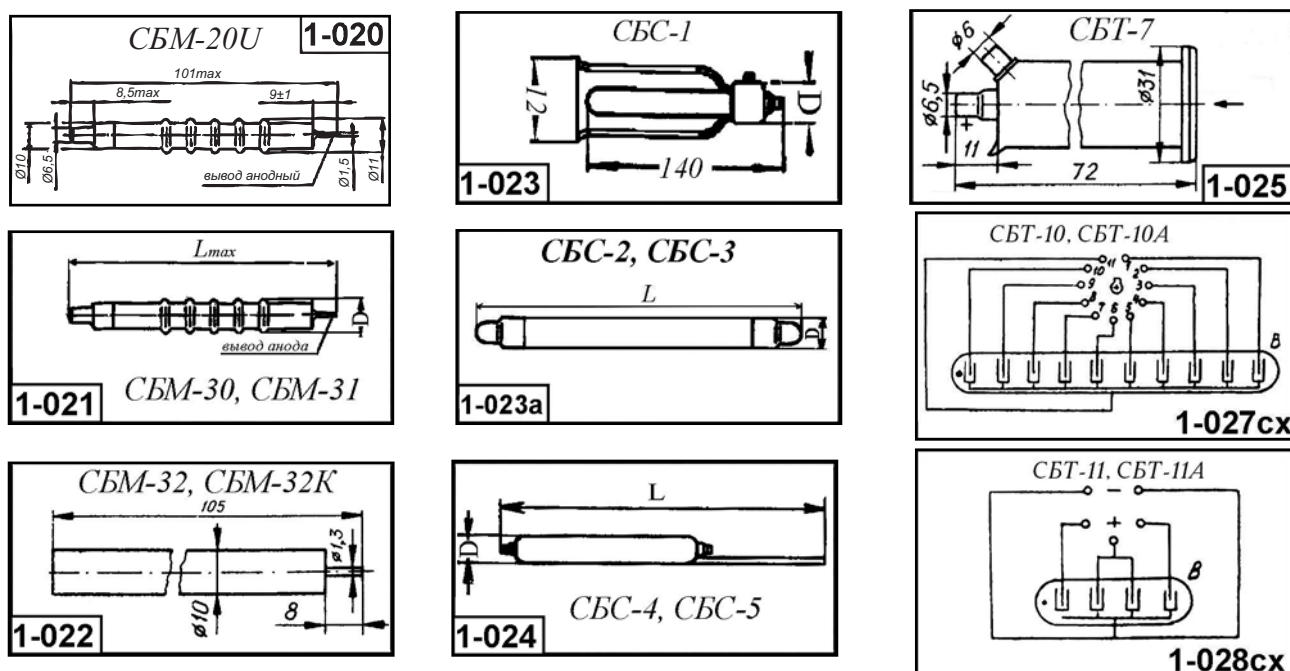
Внешний вид и габаритные размеры счетчиков и детекторов β-излучения
